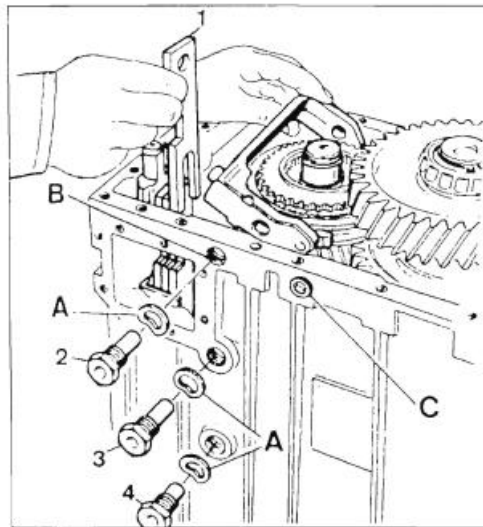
Установлення вилки 5-ї/6-ї передач:
